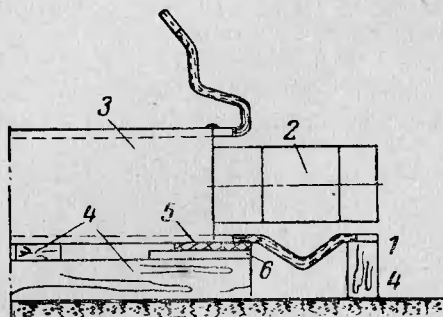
Приварка компенсаторов к шинам коробчатого профиля.
